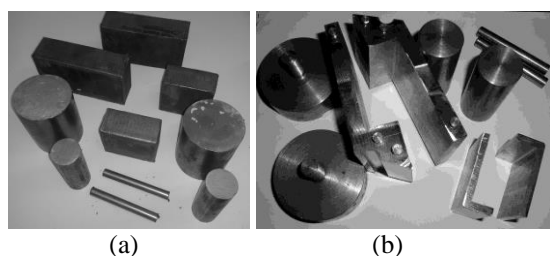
Elementos: (a) Material bruto; (b) Peças usinadas
